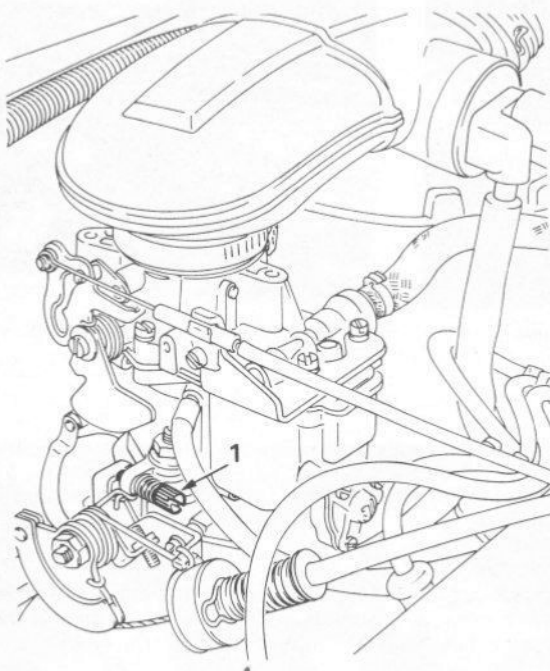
Position de la vis de ralenti (1) - carburateur Weber 32 IBSH (Sec 8)
